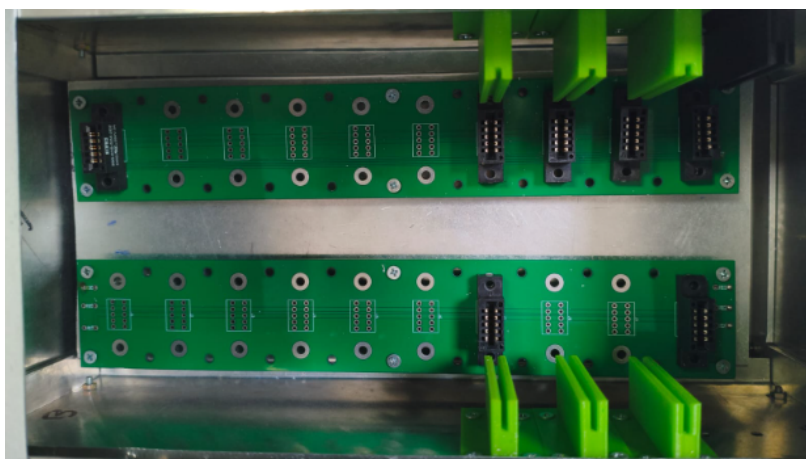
Tarjetas soldadas del Backplane
